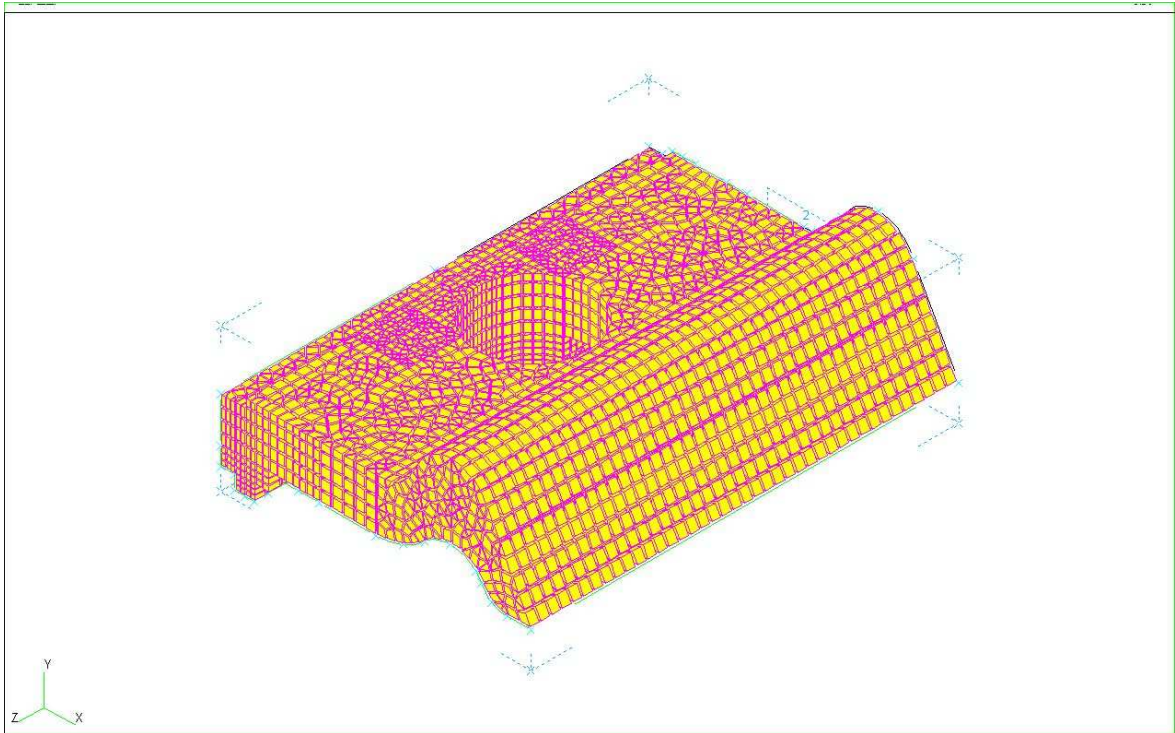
Základní geometrie úhlové vodící desky v pohledu osy Z a osy X
